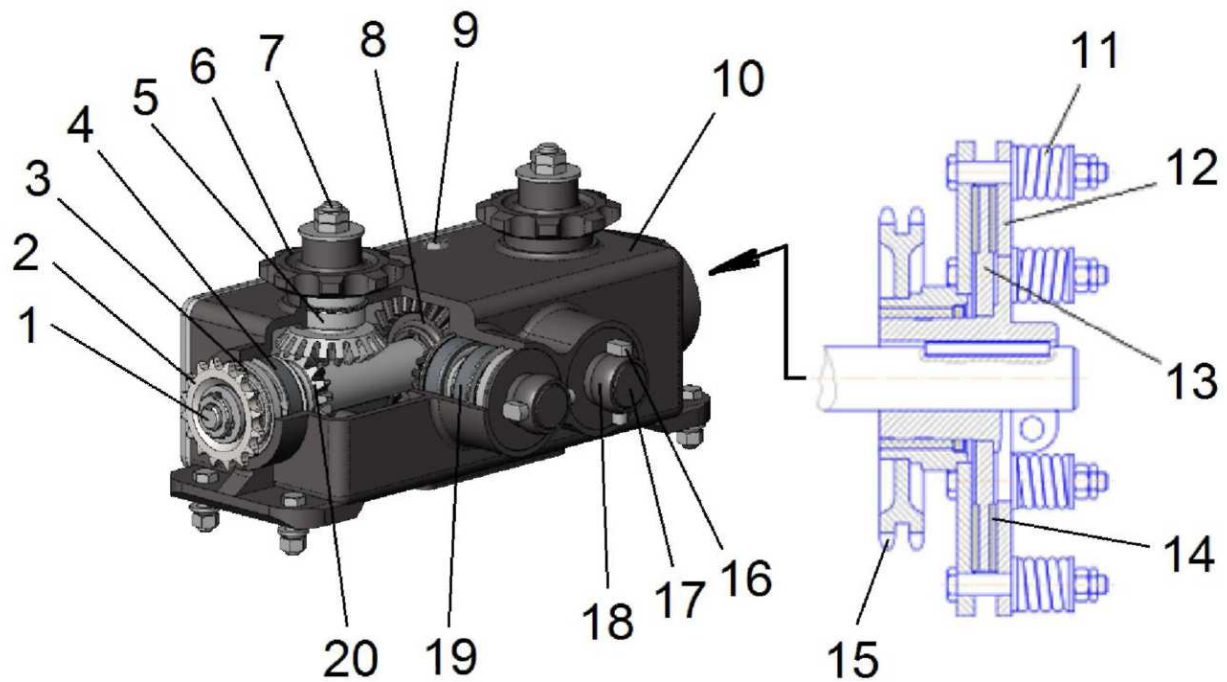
Роздавальна коробка з запобіжною муфтою: 1 – вал; 2 – напівмуфта; 3 – манжета; 4, 5, 19 – підшипник; 6 – зірочка; 7, 17 – вал-шестерня; 8, 20 – колесо зубчасте; 9 – пробка; 10 – корпус; 11 – пружина; 12 – диск натискний; 13 – диск ведучий; 14 – накладка фрикційна; 15 – зірочка; 16 – поводок; 18 – шарнір
